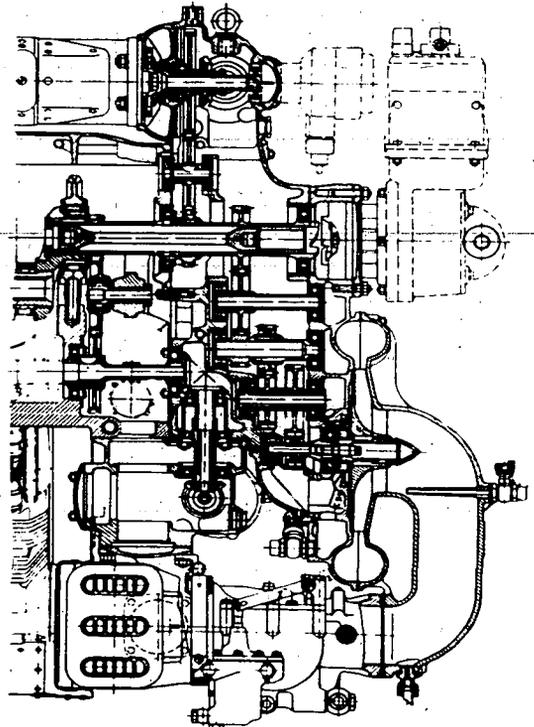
Steuerungsantrieb eines luftgekühlten 12 Zylinder-V-Motors
